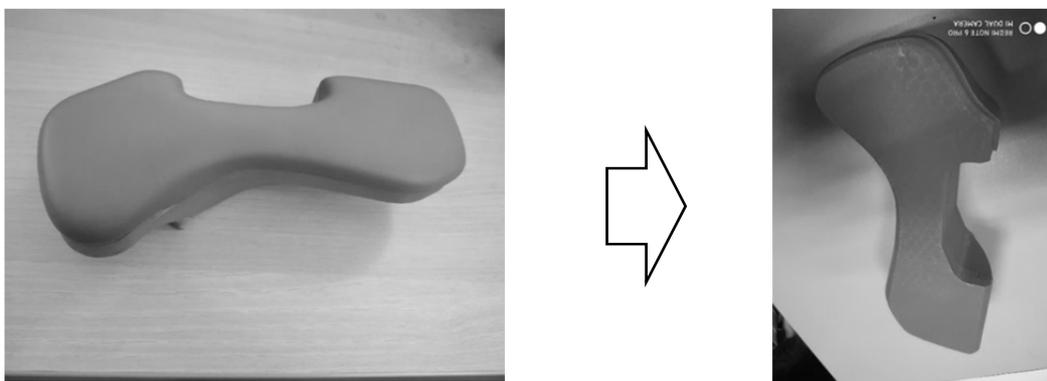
Общий вид образца рукоятки салона Unibus
